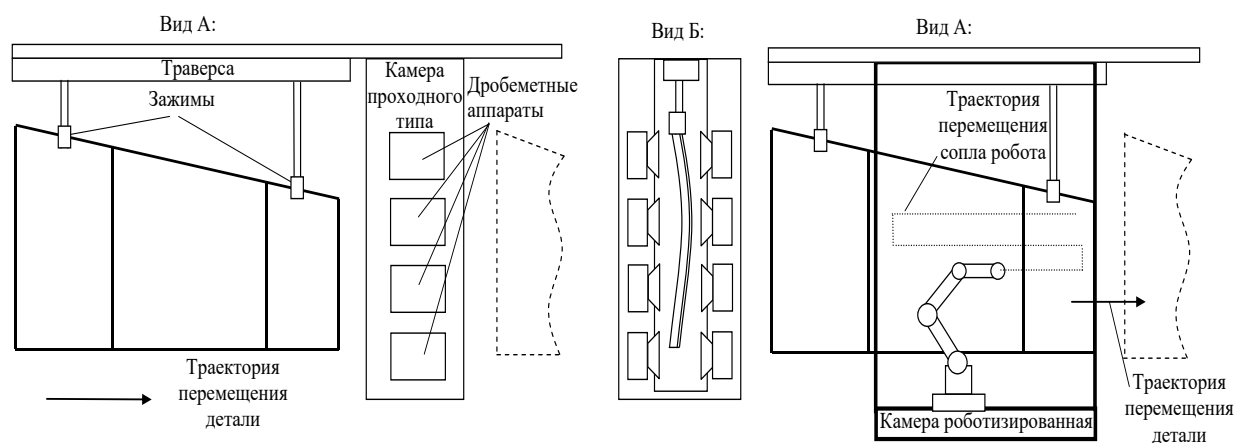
Схема дробеударного формообразования деталей на установках проходного типа:
